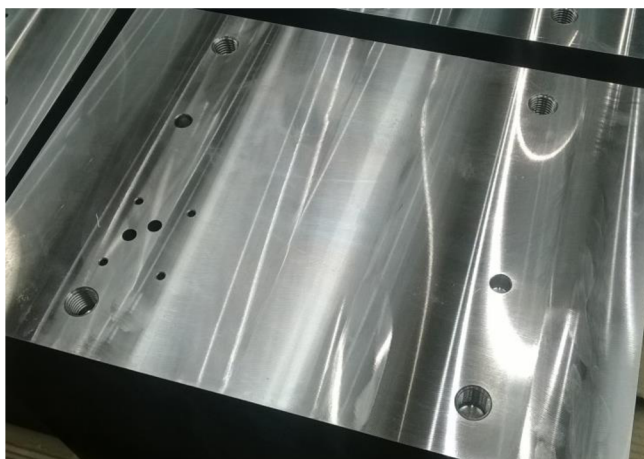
Povrch \varnothing 106 mm.Obr. 81 Hrubování \varnothing 200 mm.
